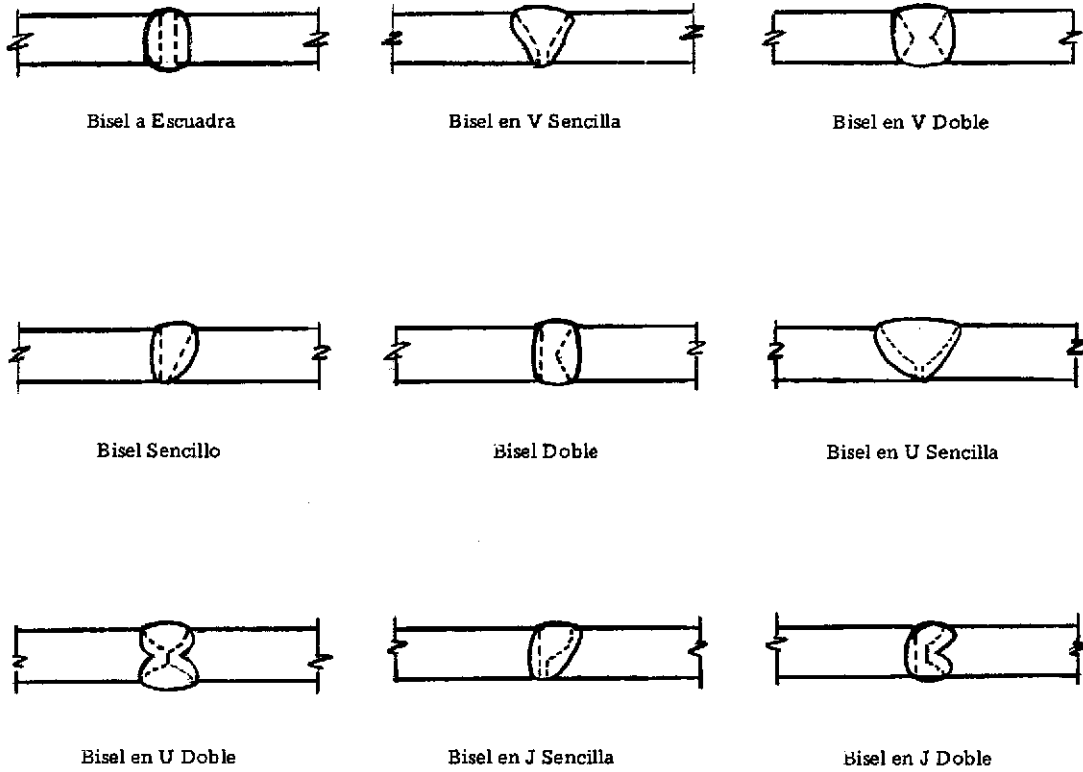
Tipos de soldaduras de bisel.
